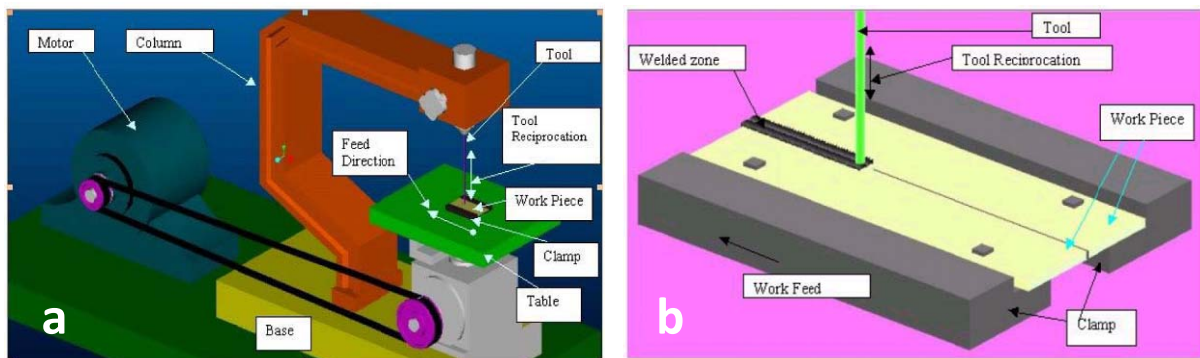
(a) Equipment und (b) Versuchsaufbau der Schweißversuche mit „Frictional Vibration“ [25 S. 5]
